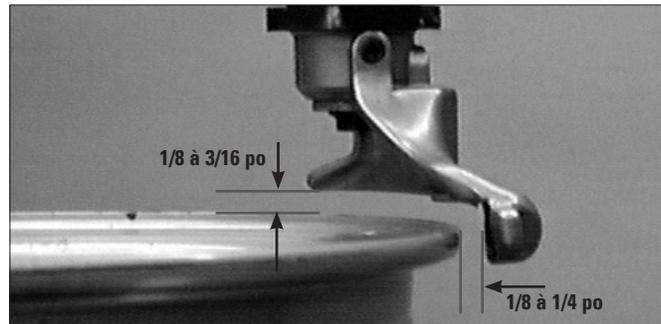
Position appropriée de l'outil de montage/démontage de roue
